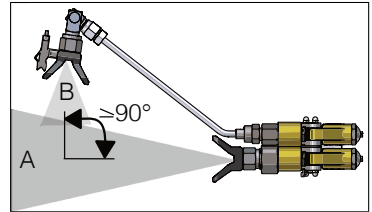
Ángulo de ajuste para la boquilla del componente B
